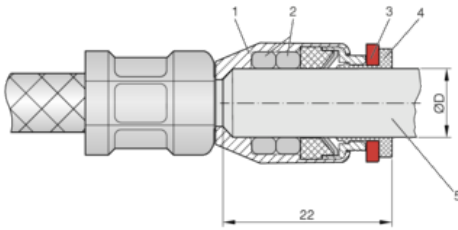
Anschlussschläuche Montage Einbau der Steckfittinge
